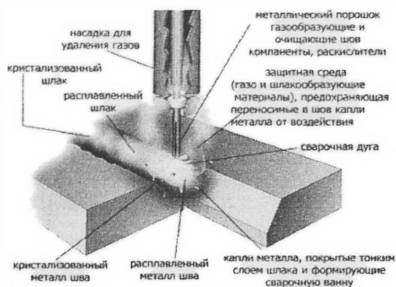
Дуговая сварка порошковыми проволоками
